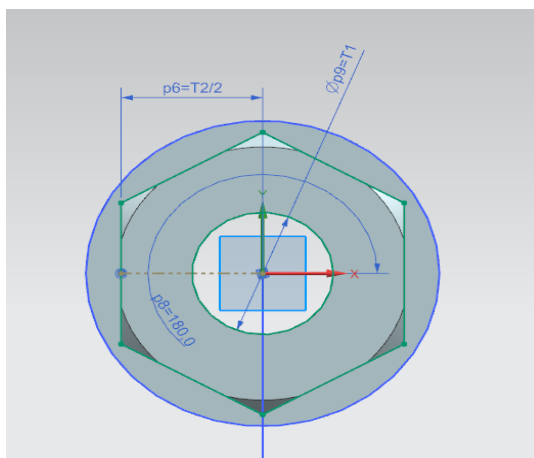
Замена размеров формулами для детали «ГАЙКА2»
